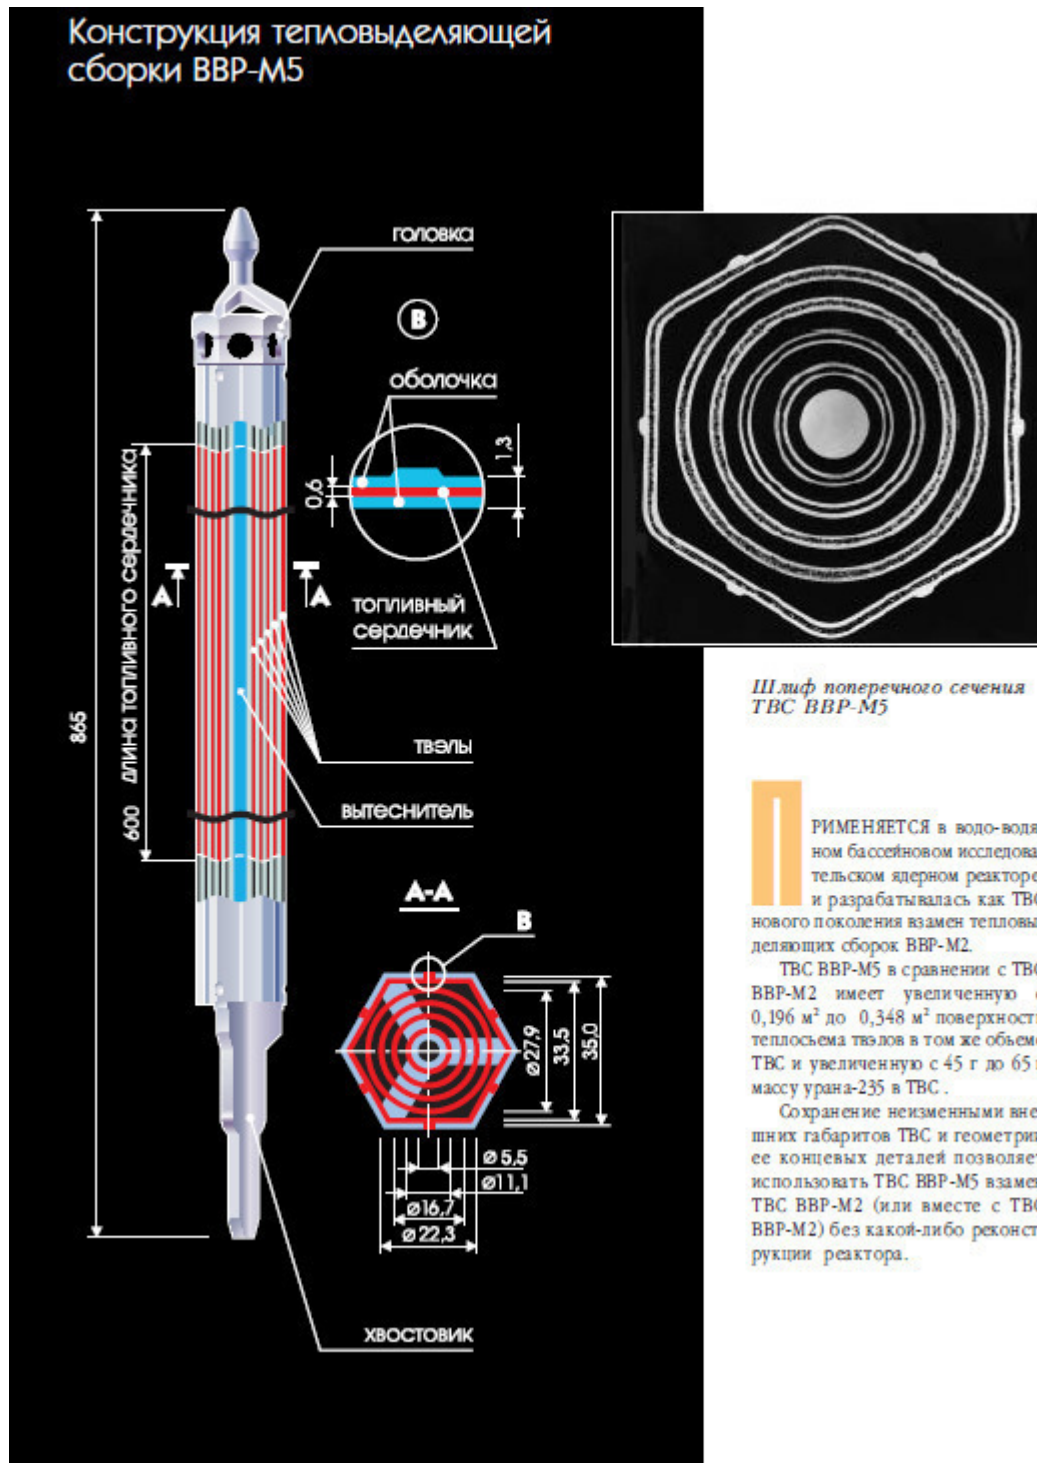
Общий вид ТВС и твэла реактора ВВР-М5
